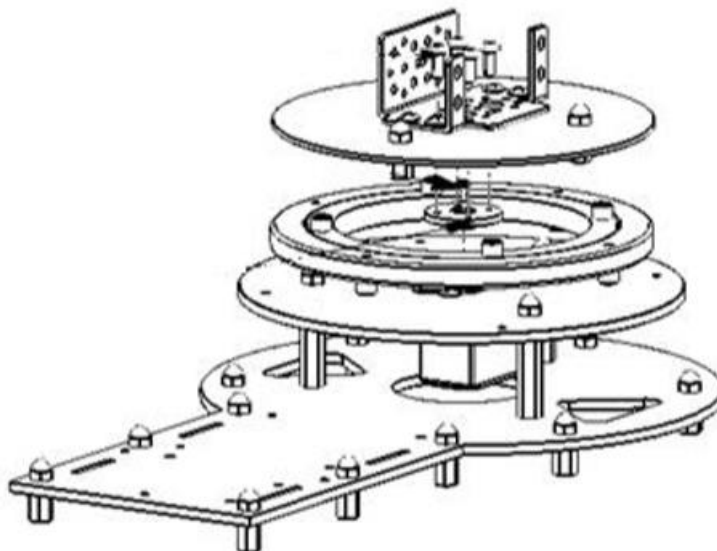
Внешний вид части платформы манипулятора
